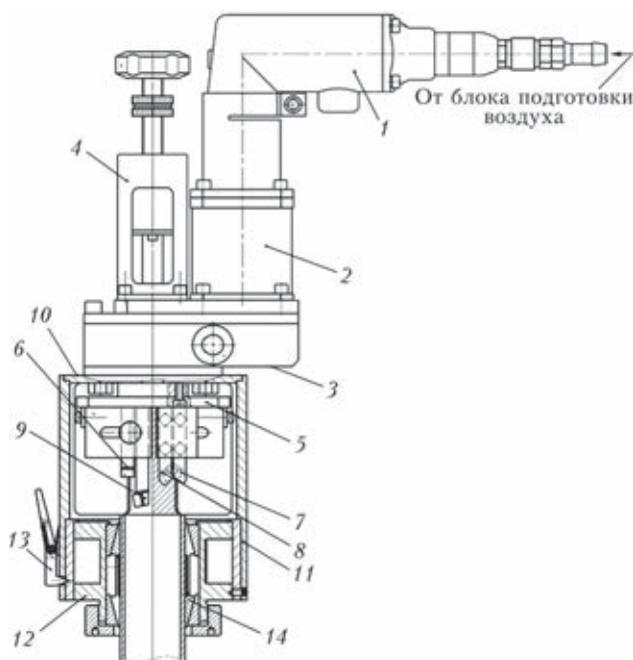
Конструктивная схема торцевателя с механизмом самоцентрирования: 1 — привод (пневмодвигатель); 2 — редуктор; 3 — неподвижный корпус; 4 — механизм подачи; 5 — планшайба; 6–9 — резцы подрезной, проходные (для формирования внешней и внутренней фасок соответственно); 10 — головка; 11 — неподвижный корпус головки; 12 — механизм базирования; 13 — быстродействующие подпружиненные фиксаторы; 14 — механизм самоцентрирования
